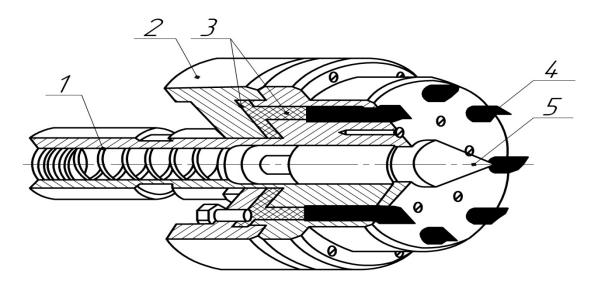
Поводковый патрон с плавающими ножами: 1 – пружина; 2 – корпус; 3 – гидропласт; 4 – нож упора; 5 – центр
